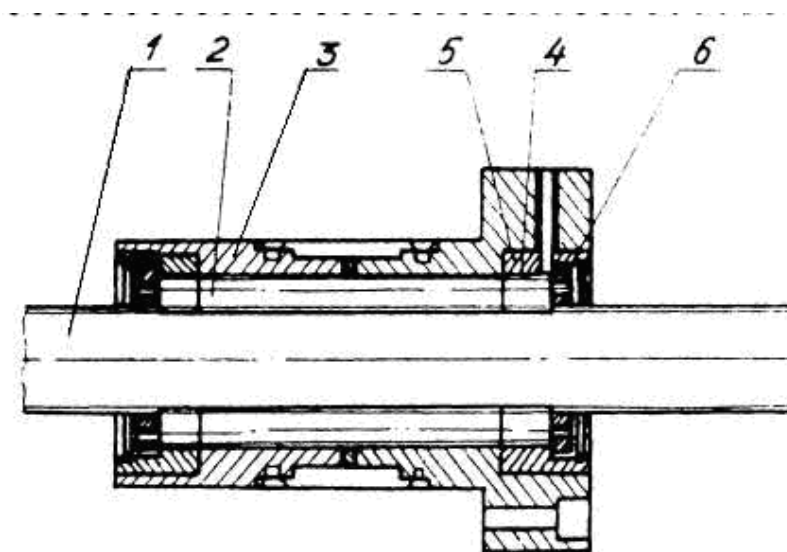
Передача винт-гайка с короткими резьбовыми роликами и двумя гайками с выборкой зазора
